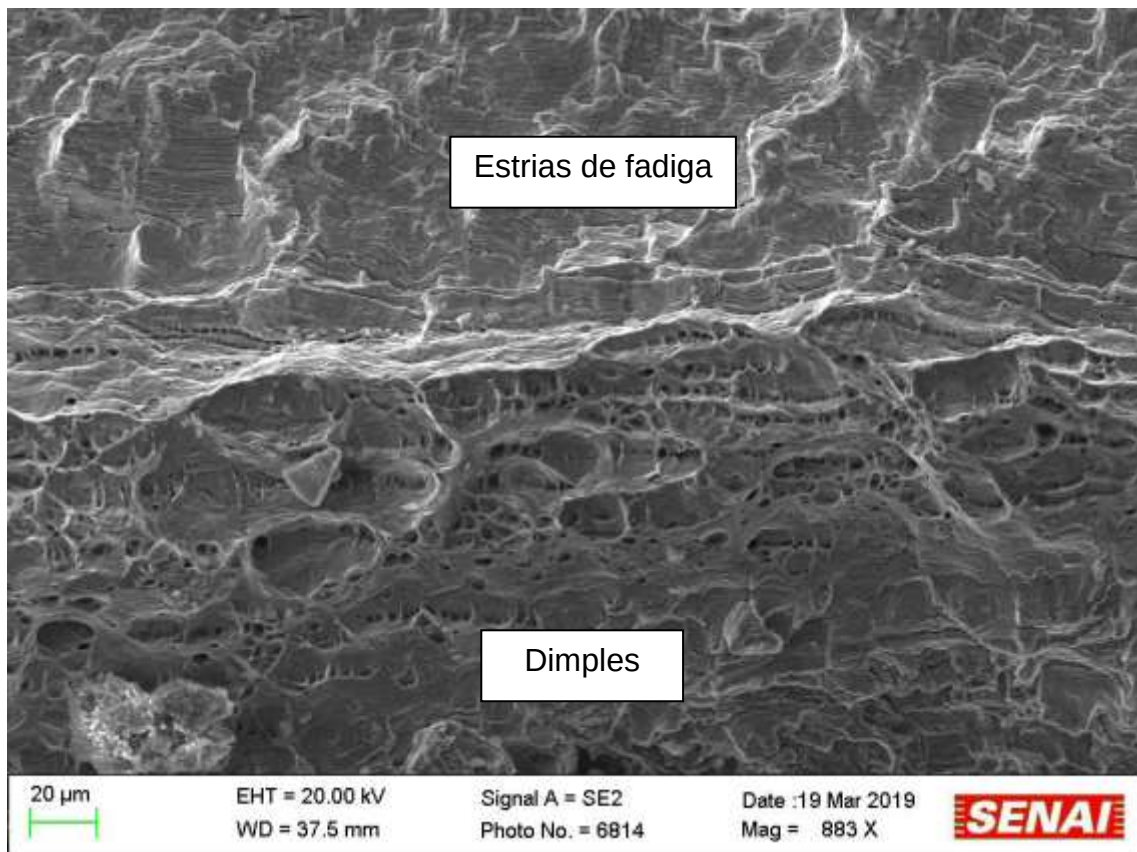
Linha de separação entre superfície fraturada e superfície destacada.
